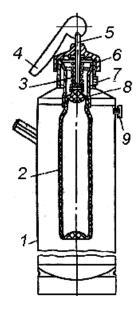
Химический пенный огнетушитель ОХП–10: 1 – корпус; 2 – стакан; 3 – пружина;4 – рукоятка; 5 –шток; 6 – крышка; 7 – спрыск; 8 – пробка; 9 – предохранительный клапан
